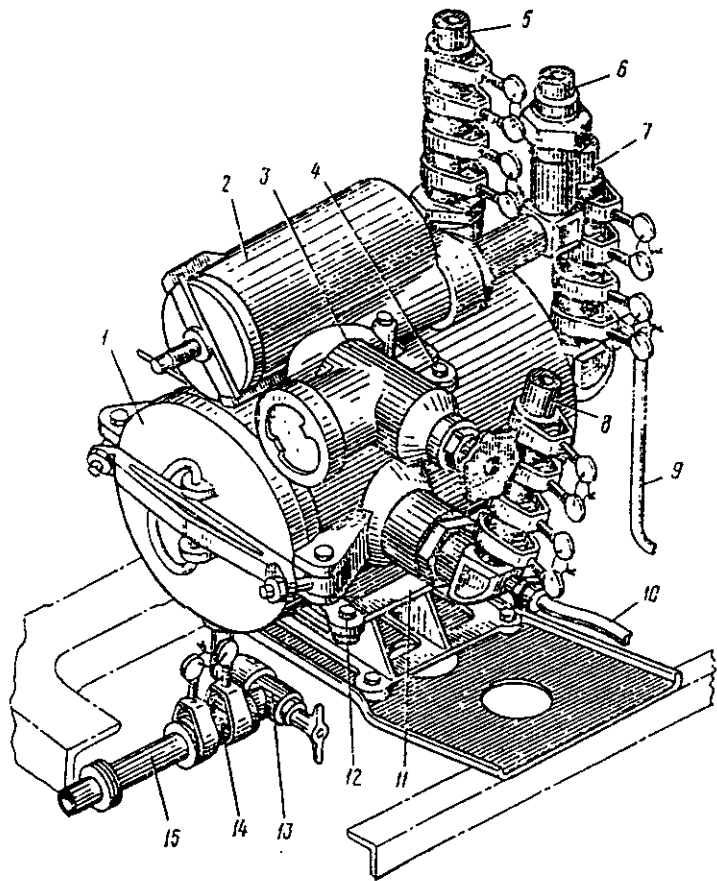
Установка корпусов фильтров грубой и тонкой очистки:
